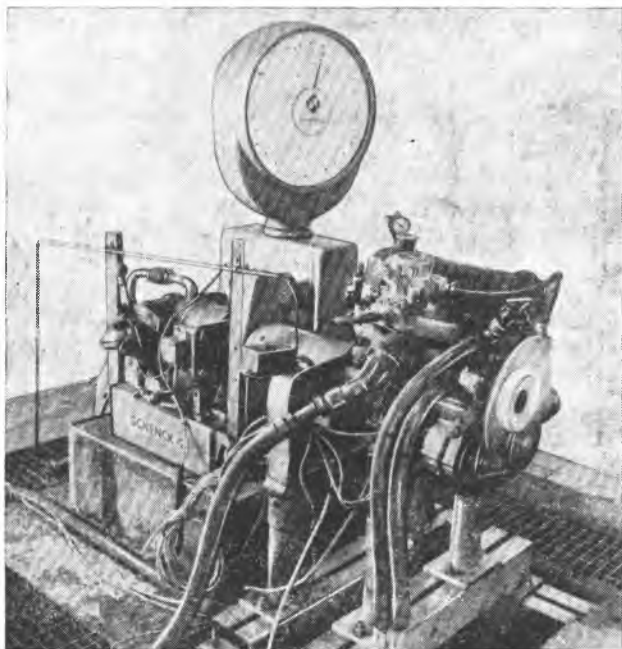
Стенд для обкатки и контроля двигателя с нагрузочным устройством и приборами для снятия характеристик
